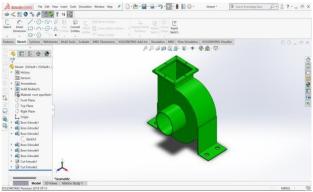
Desain 3D Sambungan Pipa Out-left
